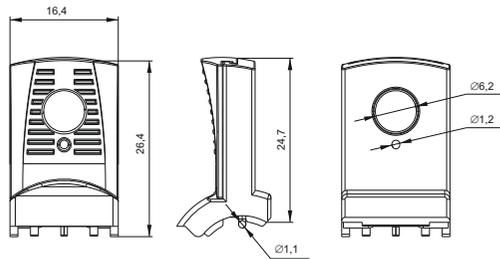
Габаритные размеры блокировки / Figure 1 – Overall dimensions of the lock
